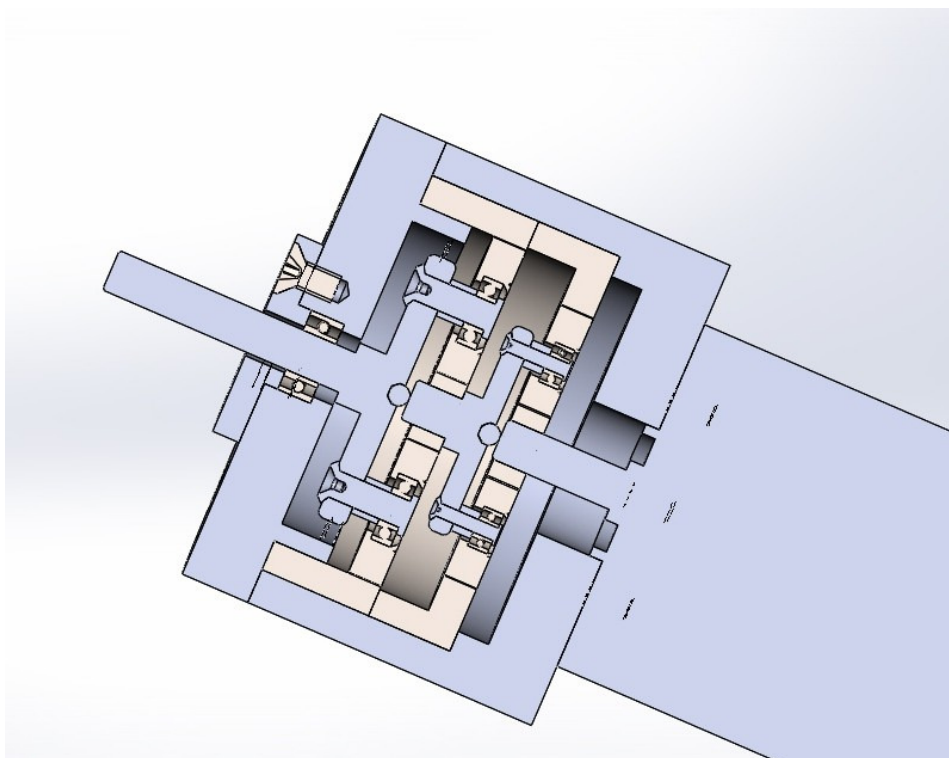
Двухступенчатый редуктор привода управления поворотной платформой
